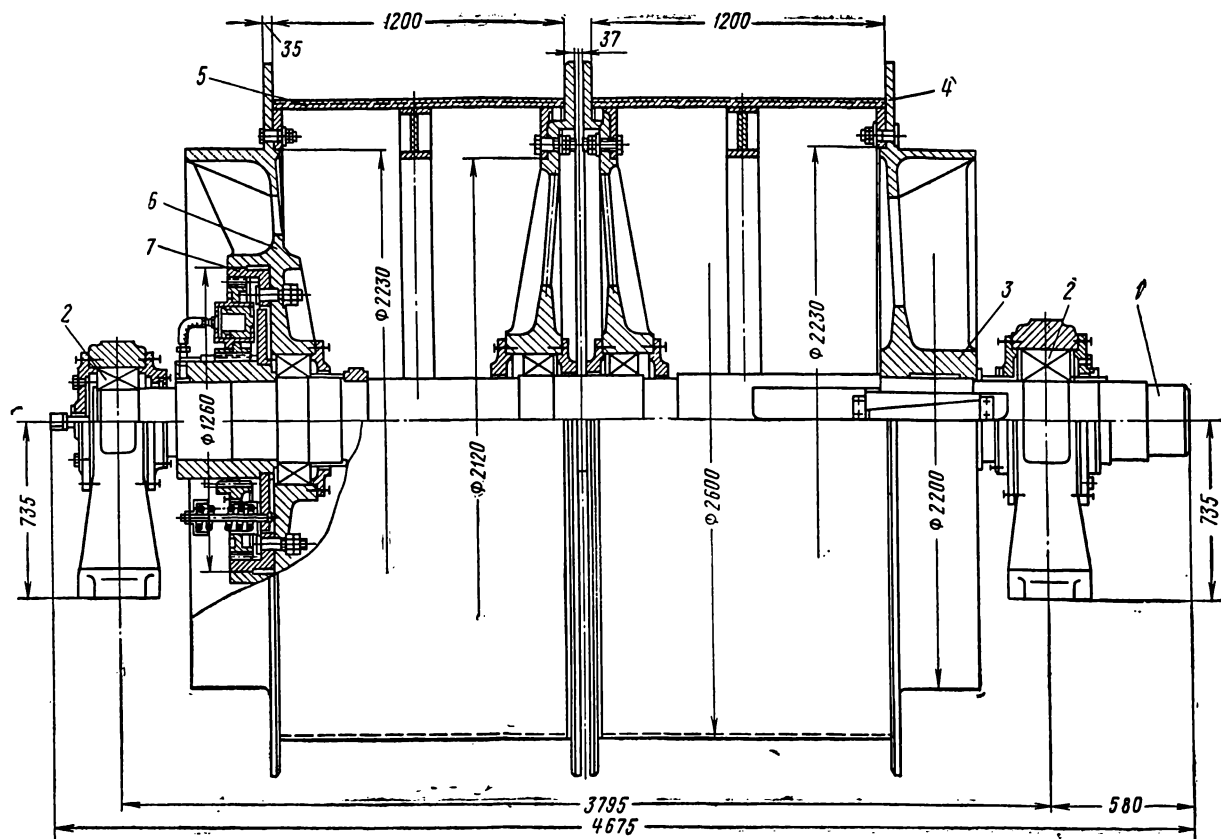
Сборка главного вала машины 2×2,5×1,2:
